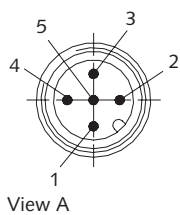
Abmessungen Schweisskraft-Prüftransmitter Typ 9833C3...
